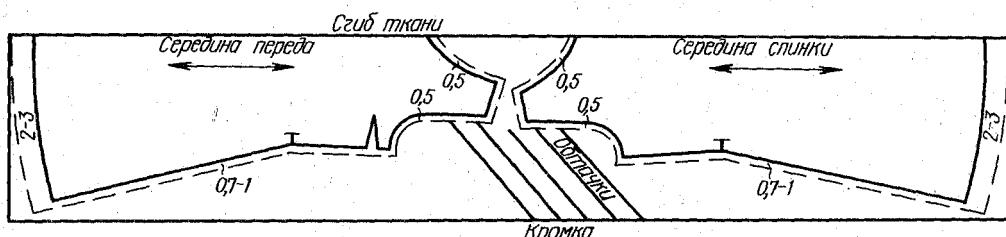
Раскладка выкроек на ткани и раскрой сорочки с цельнокроеными плечиками
